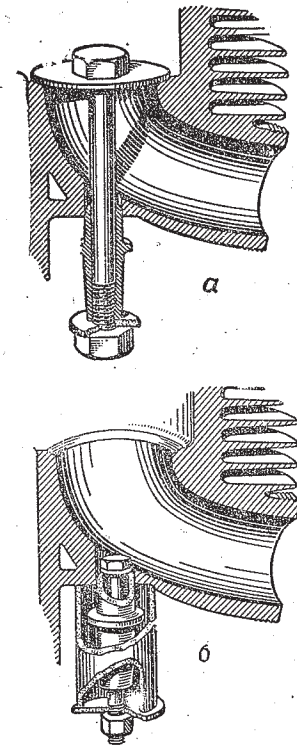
Приспособления для монтажа направляющих втулок клапанов:
